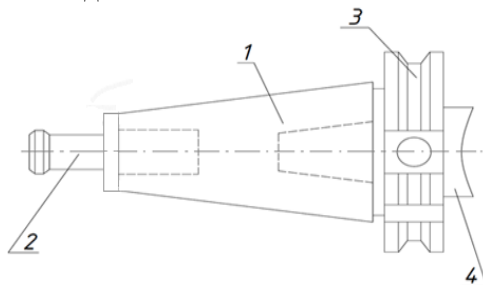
Типовые элементы конструкции фрезерной оправки
